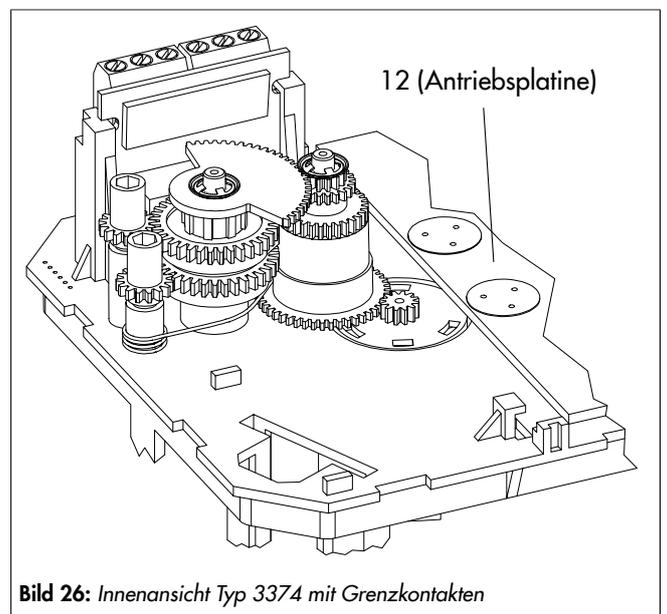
Innenansicht Typ 3374 mit Grenzkontakten
